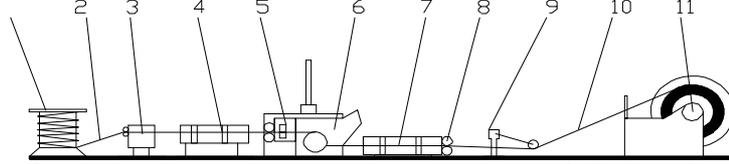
Схема компоновки оборудования линии непрерывного прессования по способу Конформ: 1 – размоточное устройство; 2 – заготовка; 3 – устройство правки заготовки; 4 – устройство очистки заготовки; 5 – машина «Conform»; 6 – гильотинные ножницы; 7 – устройство охлаждения и сушки пресс-изделия; 8 – устройство натяжения пресс-изделия; 9 – устройство контроля натяжения пресс-изделия при его смотке; 10 – пресс-изделие; 11 – намоточное устройство
